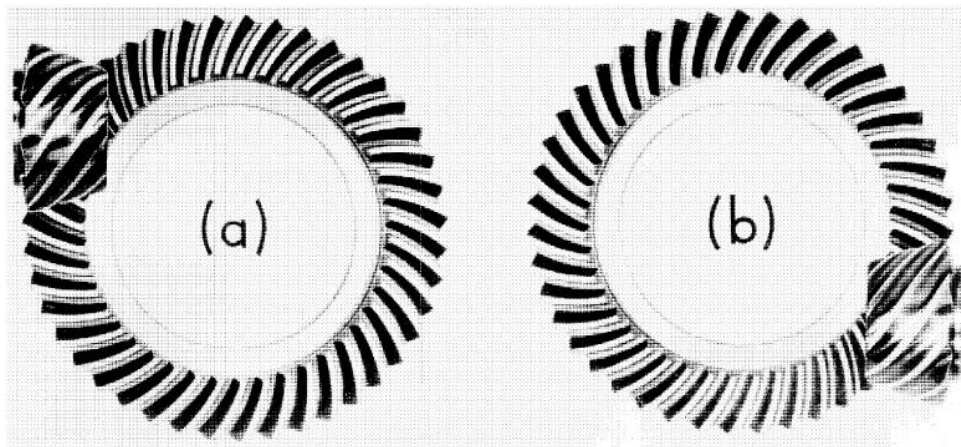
a) Engranaje derecho, b) piñón abajo del centro lado izquierdo [5].
